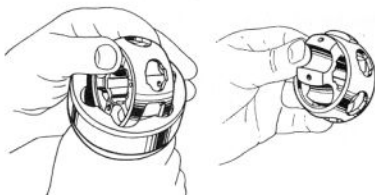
Démontage de la cage du joint de cardan "Rzeppa."
